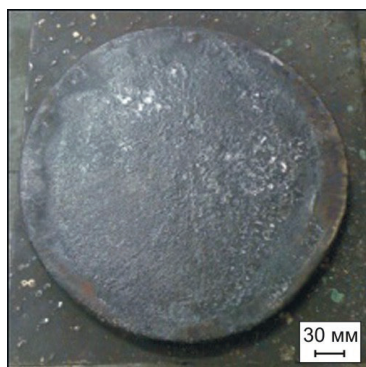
Внешний вид дисковой заготовки из опытного орто-сплава, полученной по упрощенной схеме изотермической деформации (без смены осей деформации)
